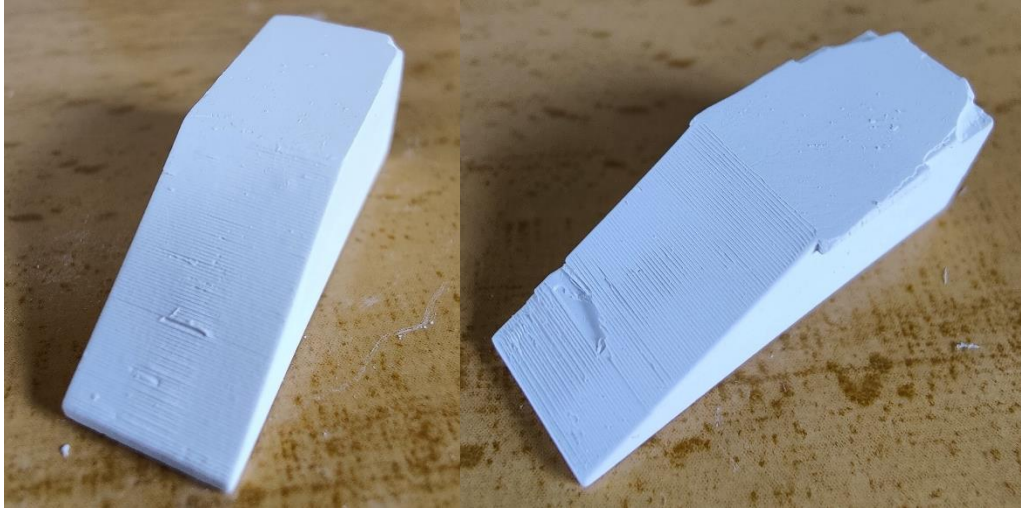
Fotografía de la pieza 8 en la que se pueden apreciar los defectos producidos tras el proceso de debinding, encontrándose a la izquierda la pieza fabricada con el segundo tipo de soporte y a la derecha la pieza fabricada con el tercer tipo de soporte.
